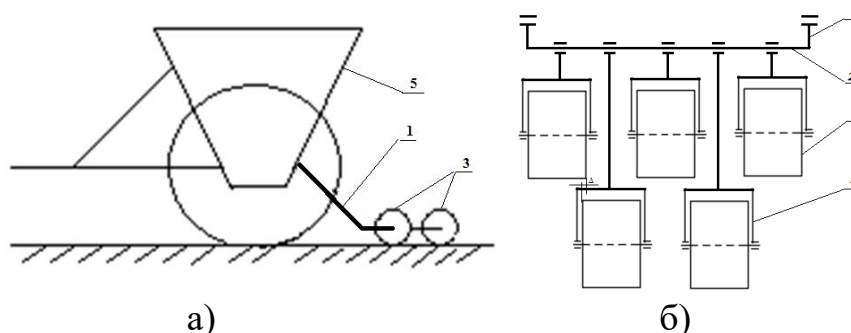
Схема экспериментальной сеялки: а – вид сбоку; б – вид сверху на прикатывающий каток 1 – тяга; 2 – ось; 3 – валец; 4 – П – образная рамка; 5 – сеялка.
